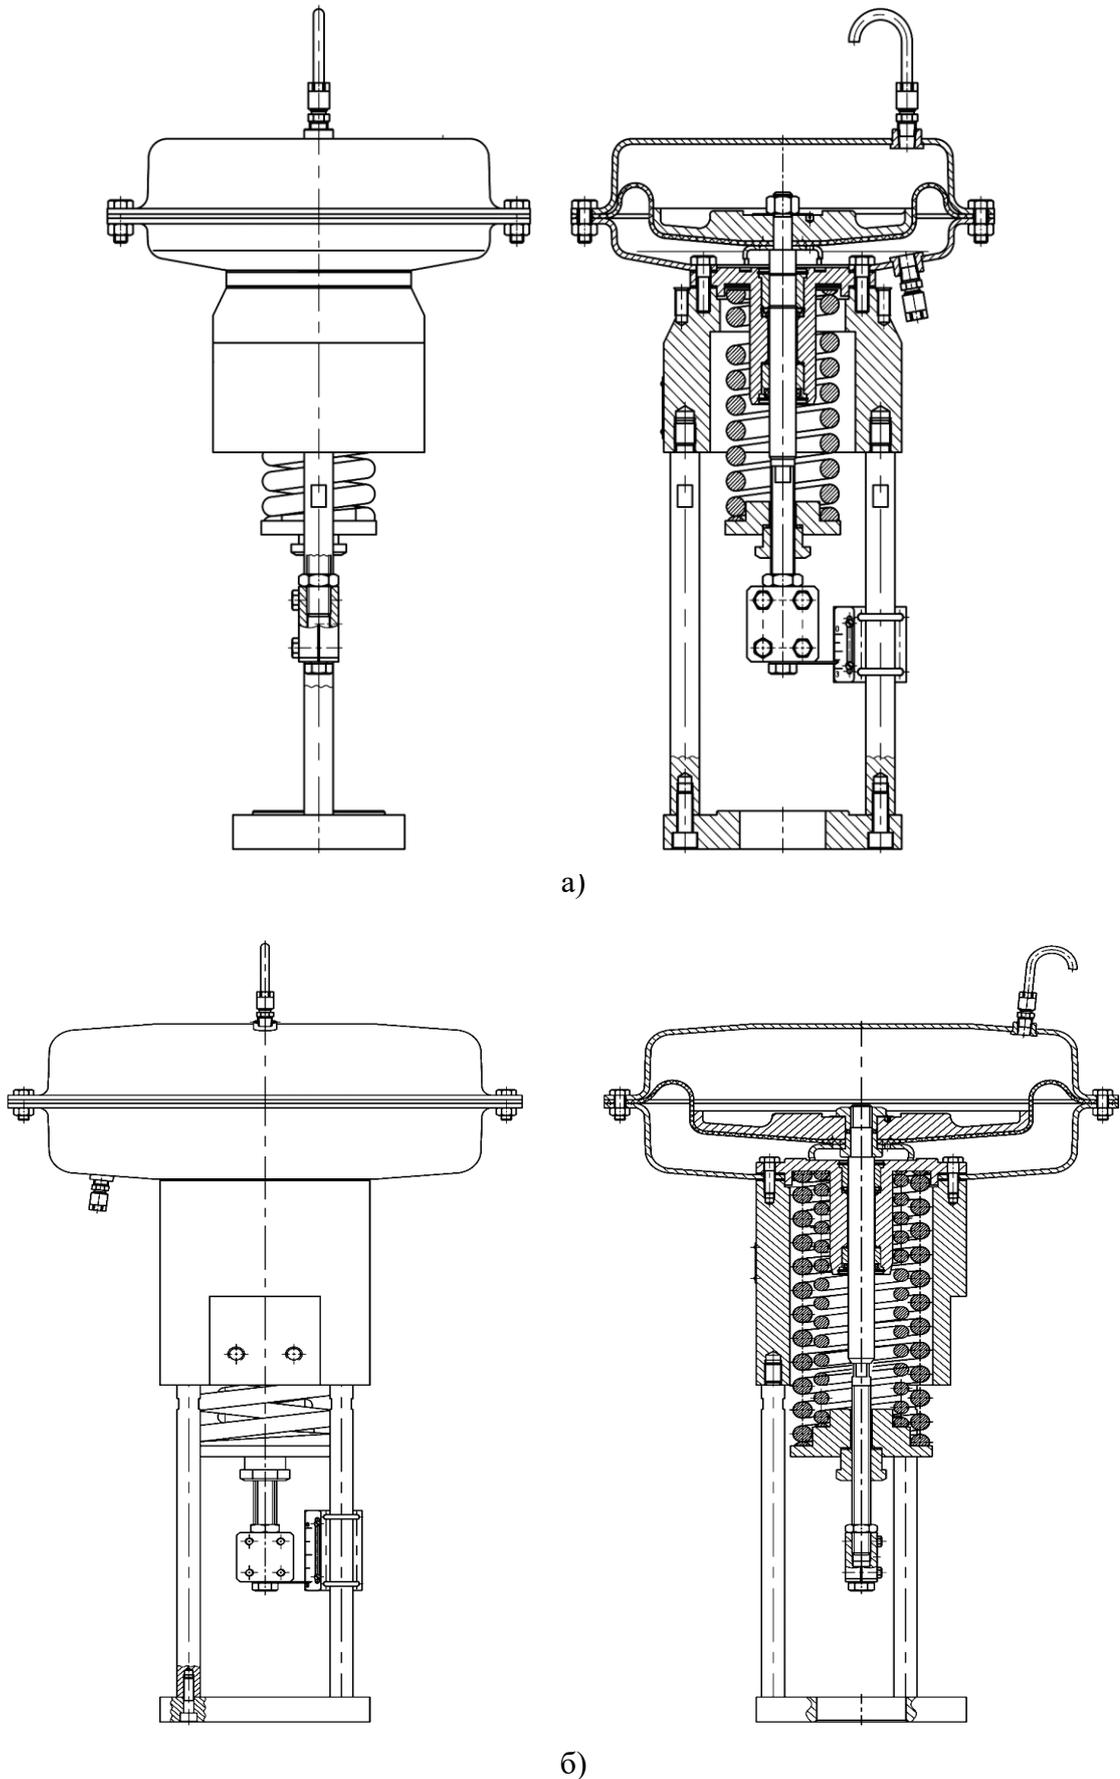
Внешний вид и конструкция механизма с  $P_{ном} = 400$  кПа обратного действия:
